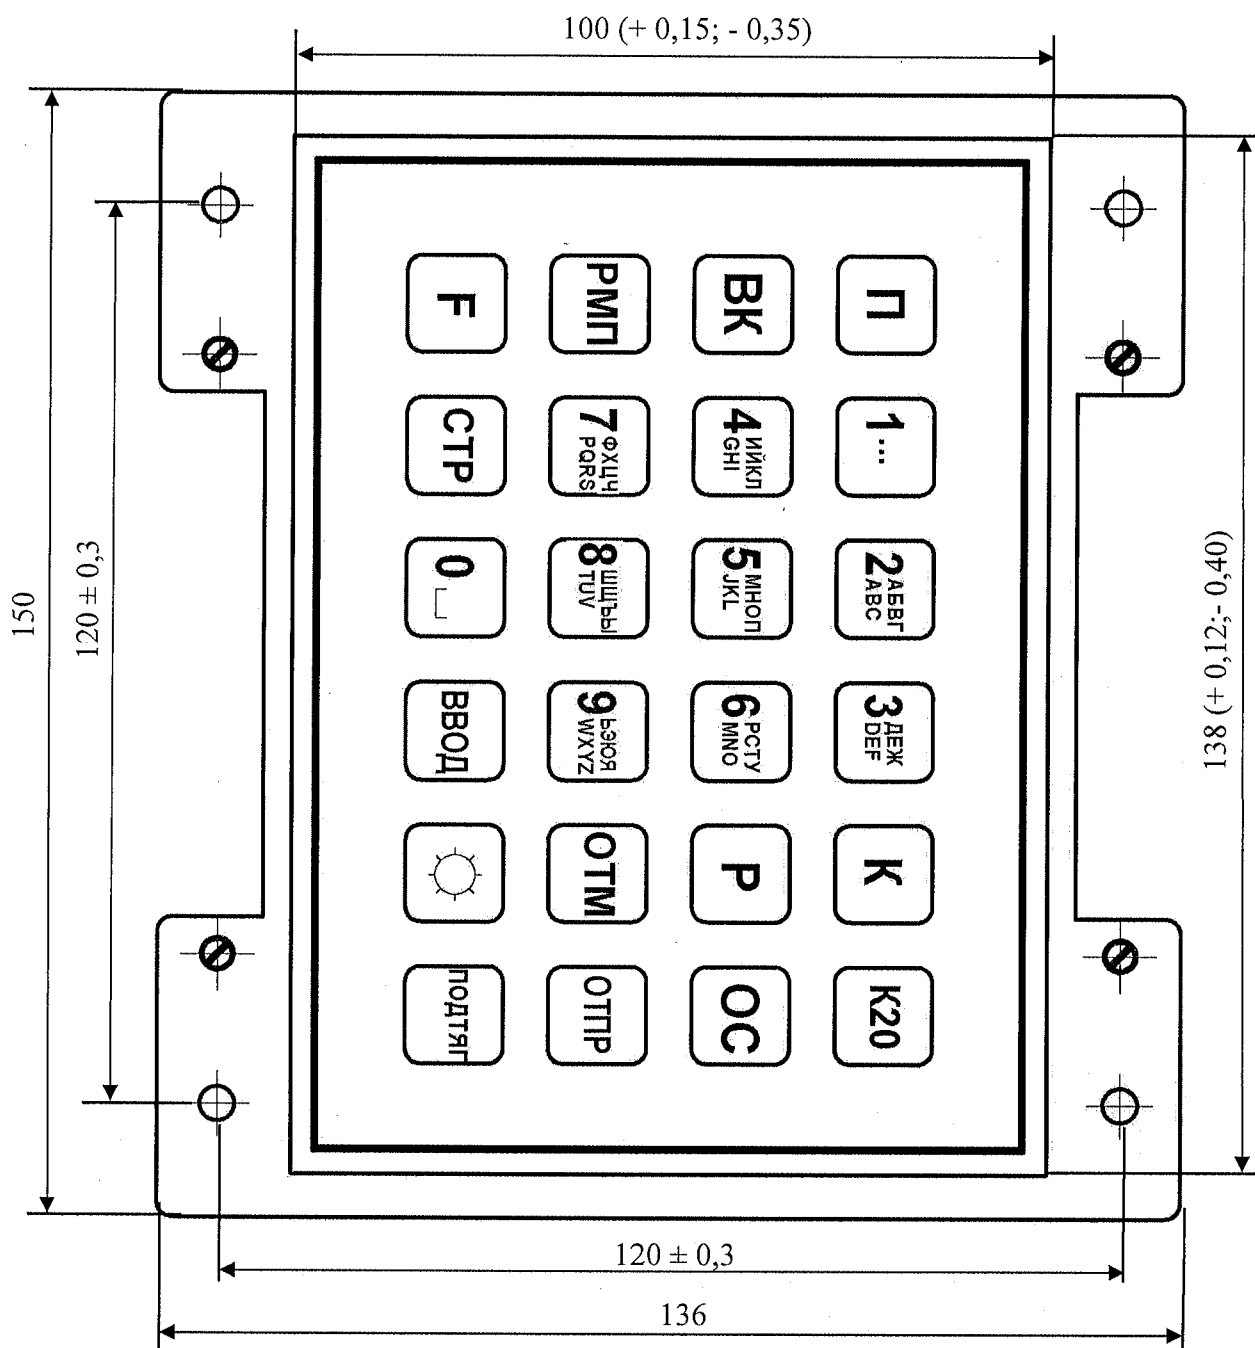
Внешний вид лицевой панели и присоединительные размеры модуля ввода 1 36905-250-00-01, модуля ввода 1М 36905-250-00-03
